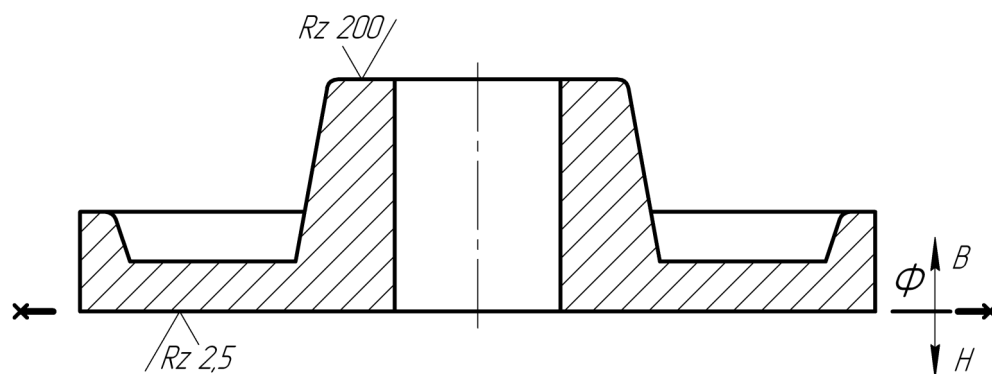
Положение ответственных обрабатываемых поверхностей отливки в форме
